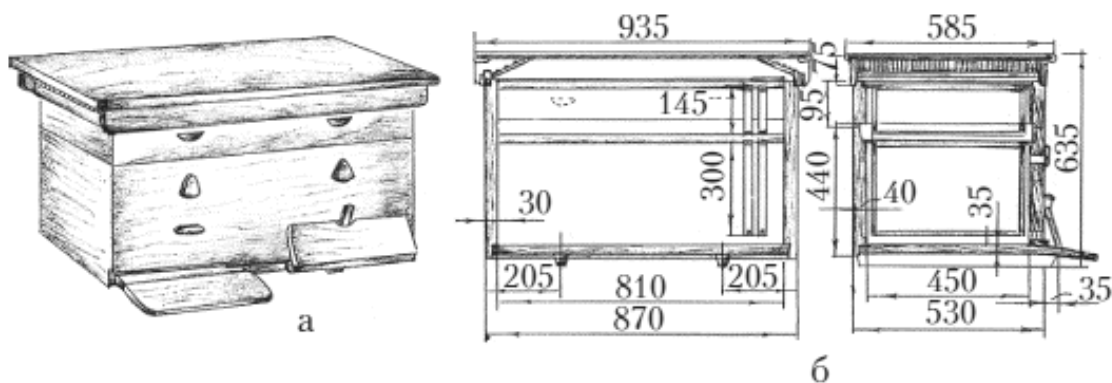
Улей-лежак: а – общий вид; б – устройство улья
